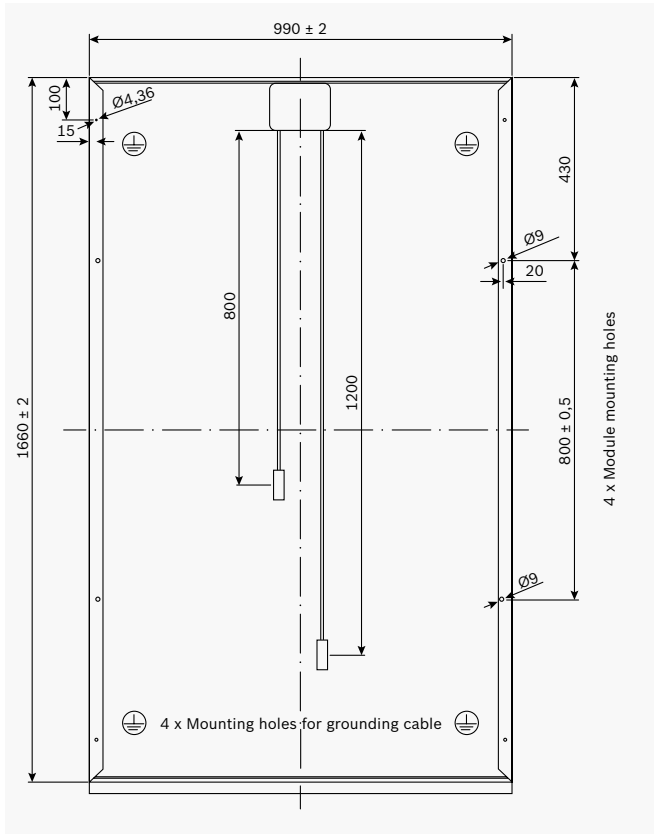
Parte posterior c-Si M 60 y M 60 S, P 60, fabricante: 14, 17 y 23
